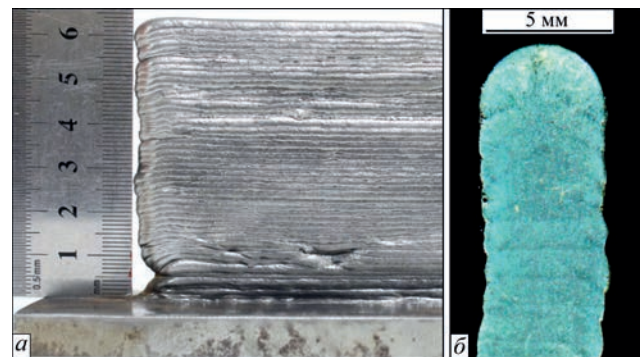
Наплавлений PAW-CW способом зразок зі сталі 09Г2С (G3Si1): а – загальний вигляд бокової поверхні; б – поперечний макрошліф
